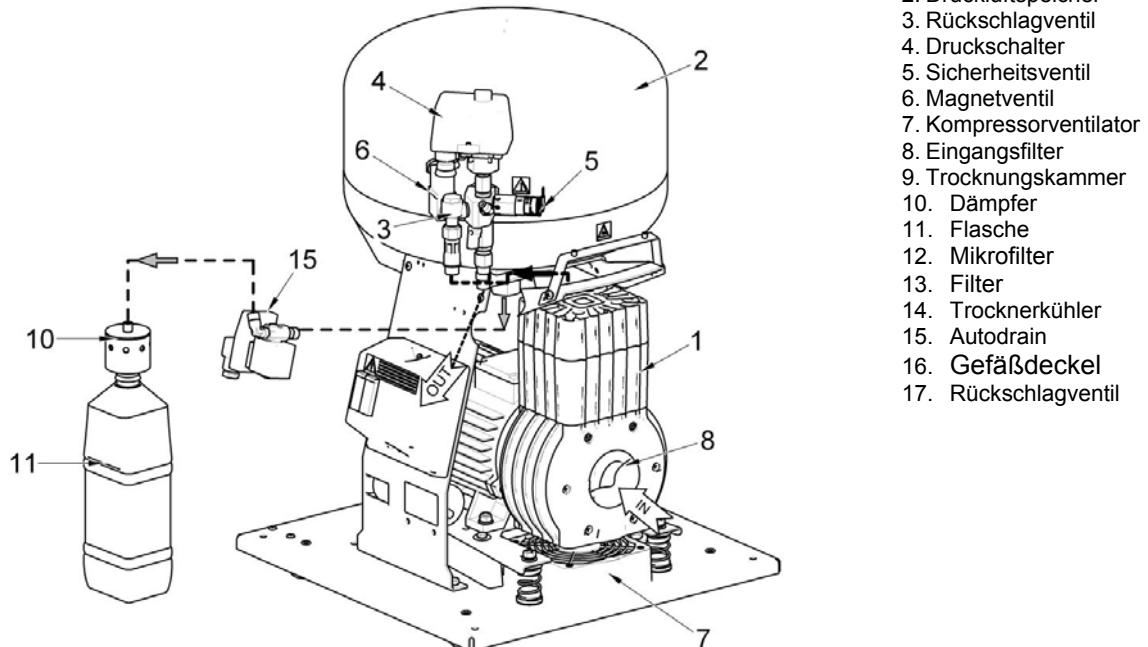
Kompressor mit Lufttrockner MONZUN – M1a
